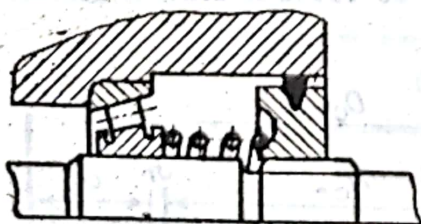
Lanț de dimensiuni cu compensator mobil continuu.
